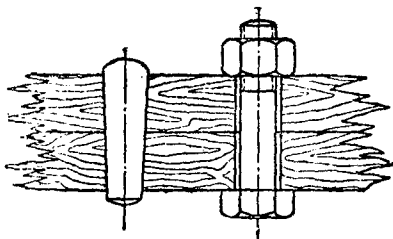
Неправильный чертеж детали в разрезе. Клин и болт не даны в разрезе.
